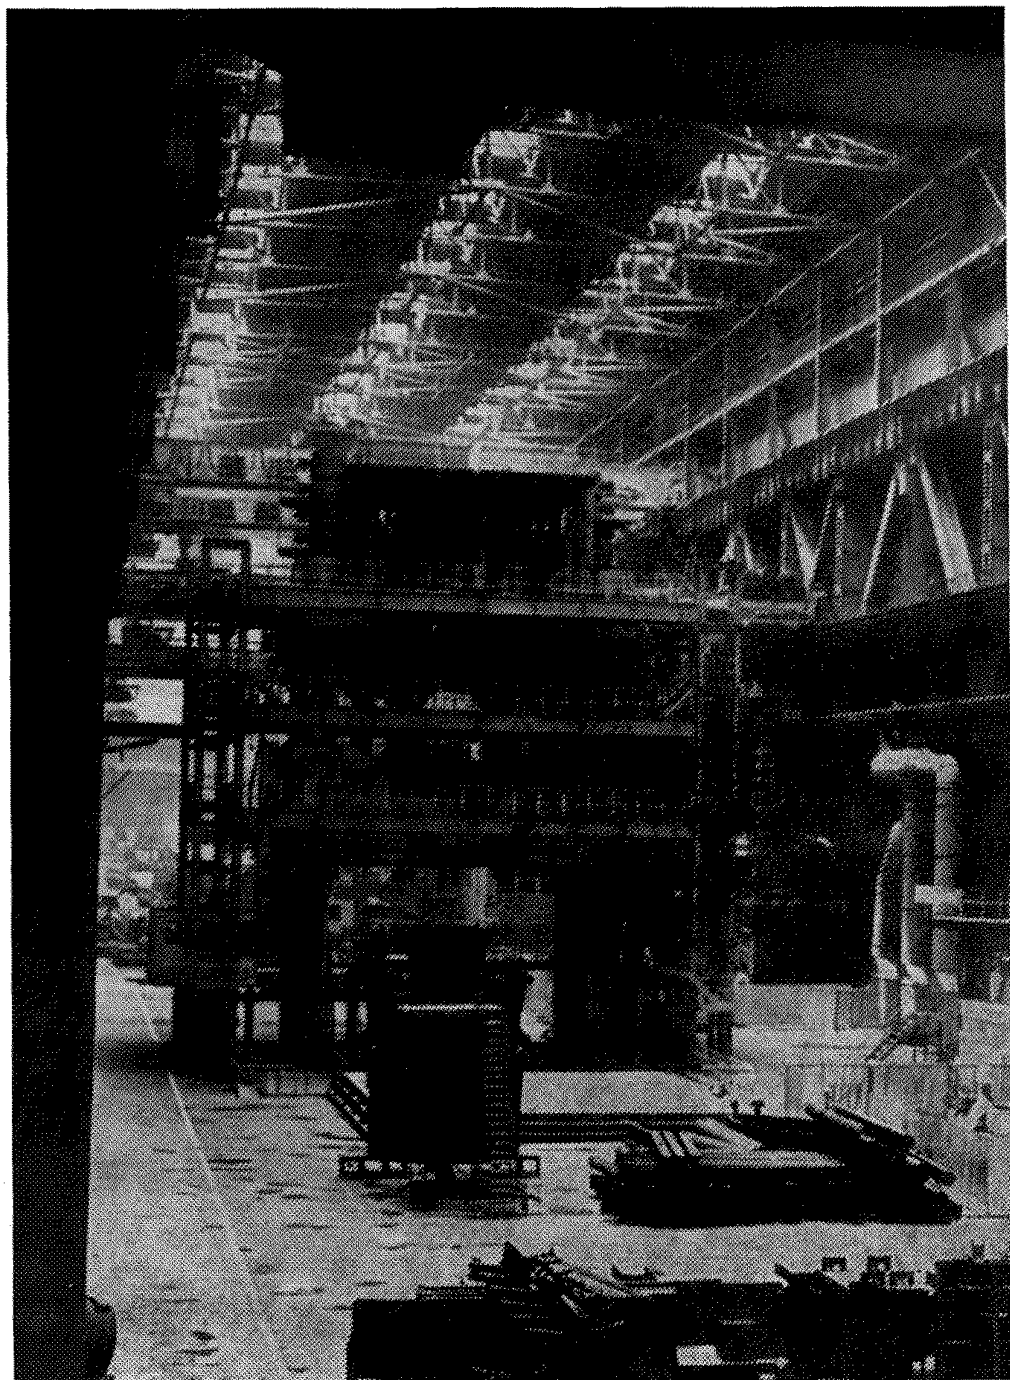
Пример центрической установки оборудования в интерьере участка гид-ропресса производственного корпуса Волго-Донского завода «Атоммаш»
